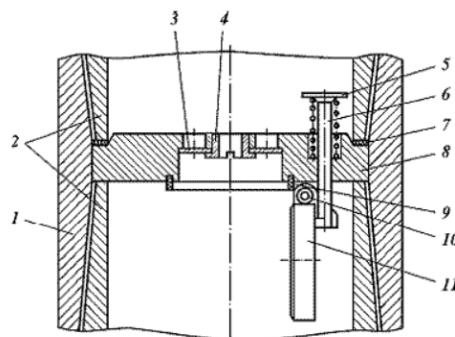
Клапан обратный бескорпусного типа КОБ для обсадной колонны [23-25]:
